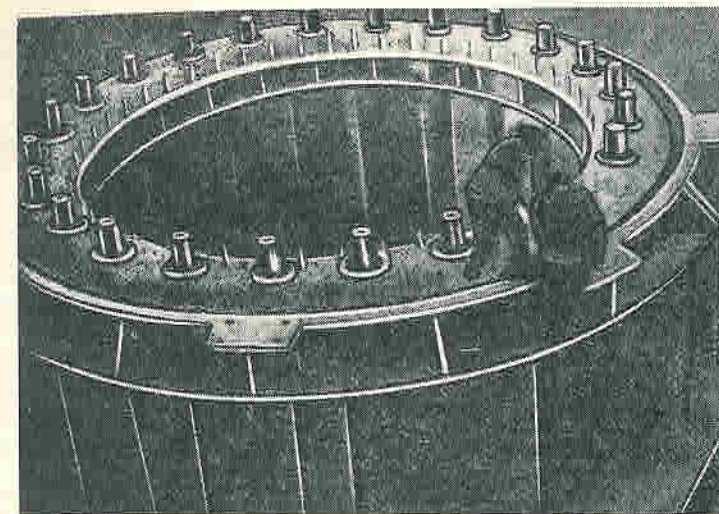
Установка и центрирование верхнего кольца направляющего аппарата
